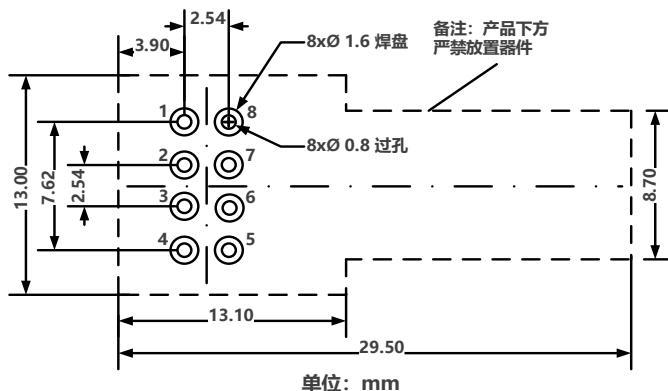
PCB Layout 设计推荐尺寸图 (俯视图)
